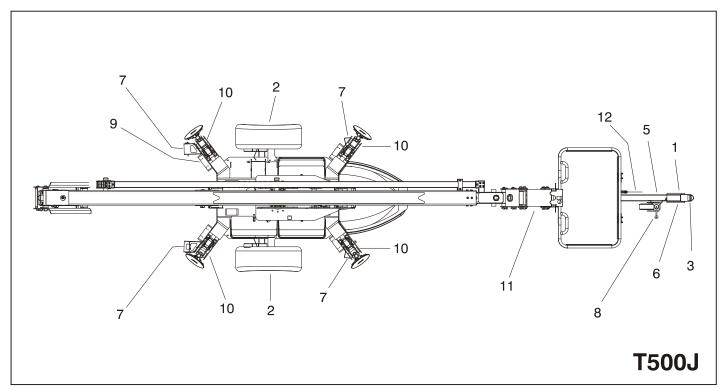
Inspección antes del remolcado - Hoja 2 de 2
